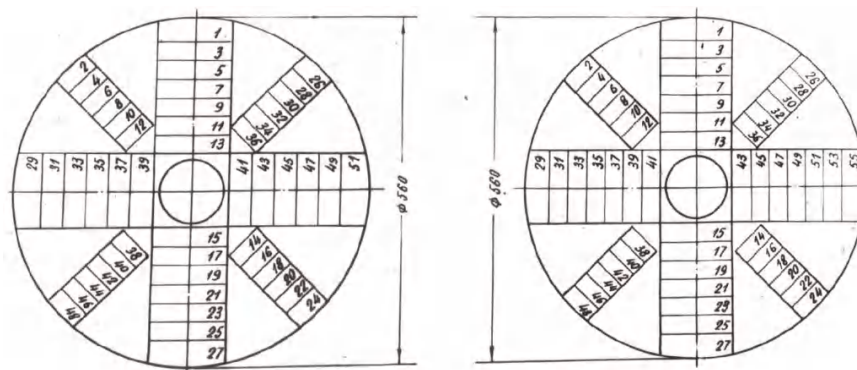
Схема вырезки образцов из диска заготовки роторного вала
